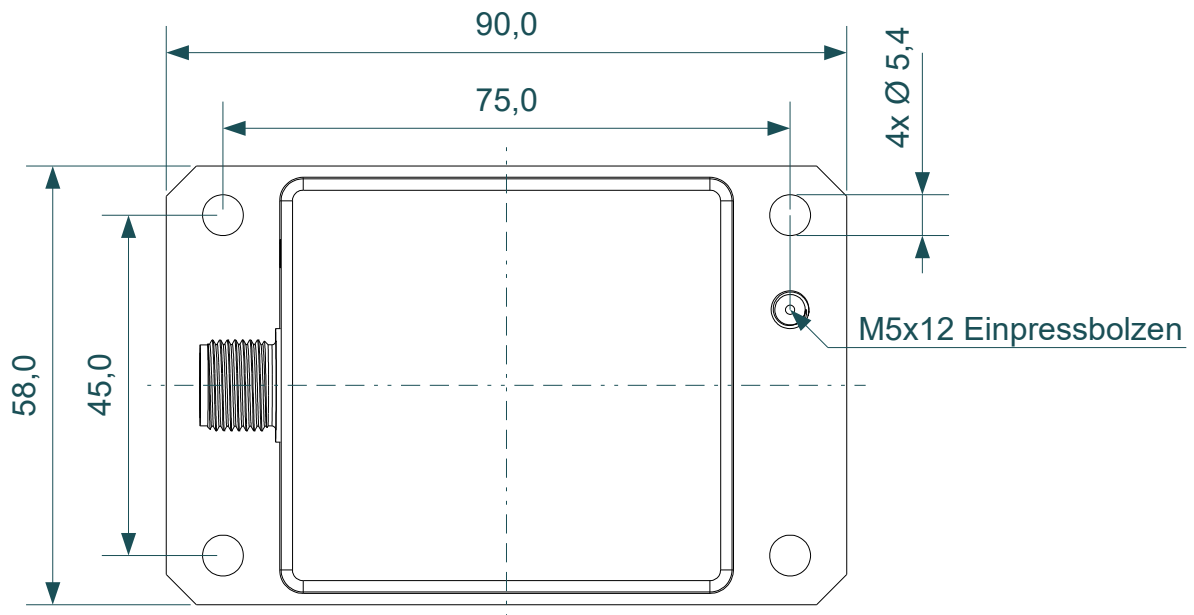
Befestigungsbohrungen Aluminiumgehäuse (MA) (Maße in mm)
